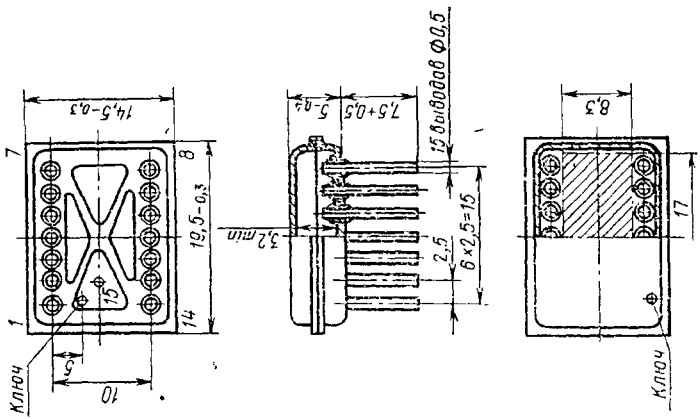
Конструкция металлоклядного корпуса 1203 (151.15-1)
